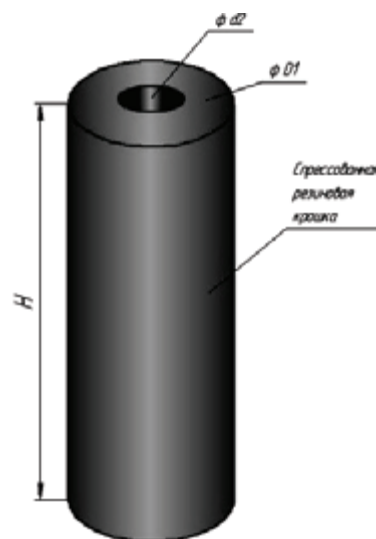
Деталь 2 – полый цилиндр из спрессованной резиновой крошки.
